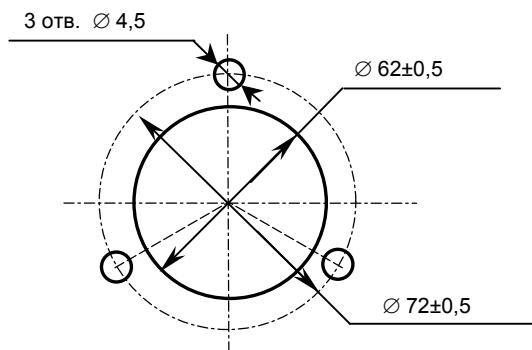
Установочные размеры штурвала LGF-12-003B-100
